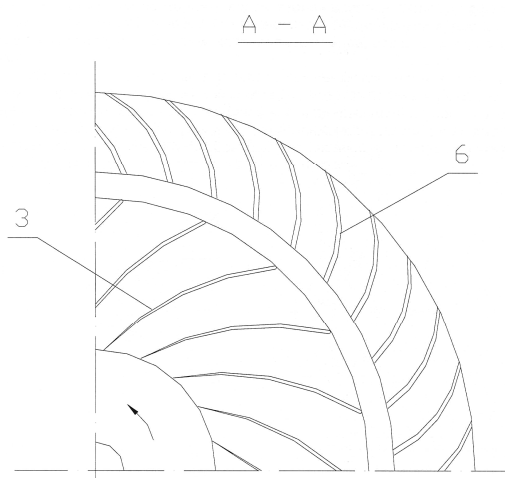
Поперечный разрез рабочего колеса центробежного компрессора А-А (см. рис. 1)
